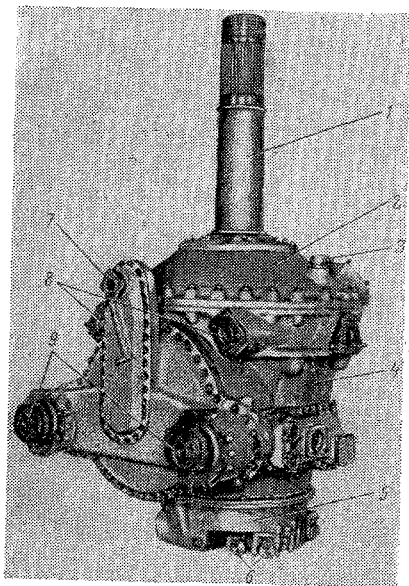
Редуктор ВР-8А (вид спереди слева):
